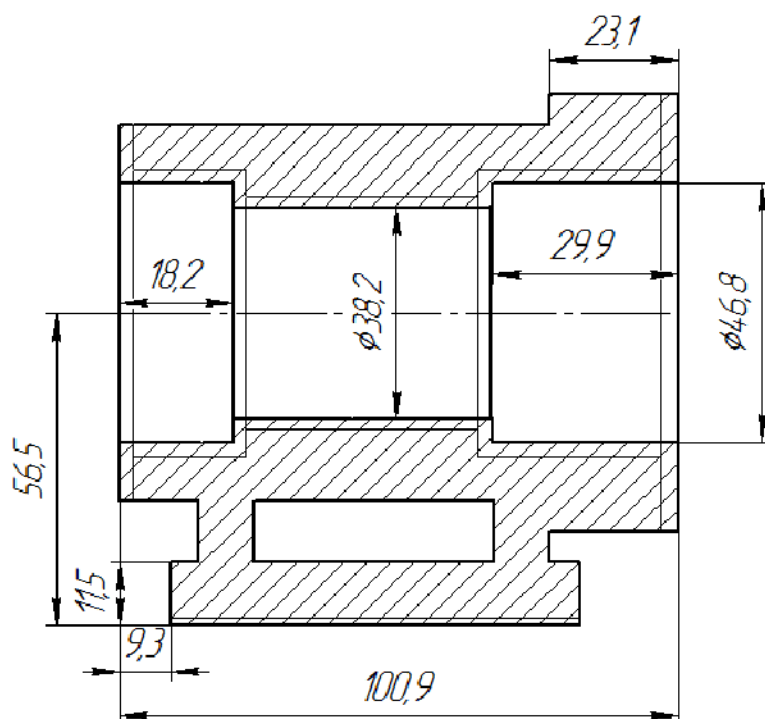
Ескіз заготовки при литті в оболонкові форми
